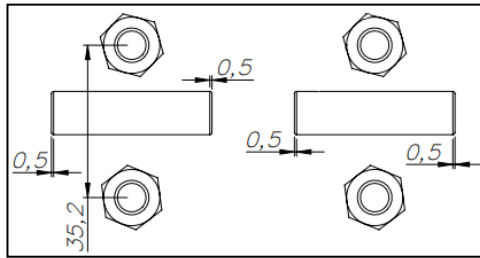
Fragment rysunku wykonawczego połączenia z luzem w dwóch kierunkach [opracowanie własne]
